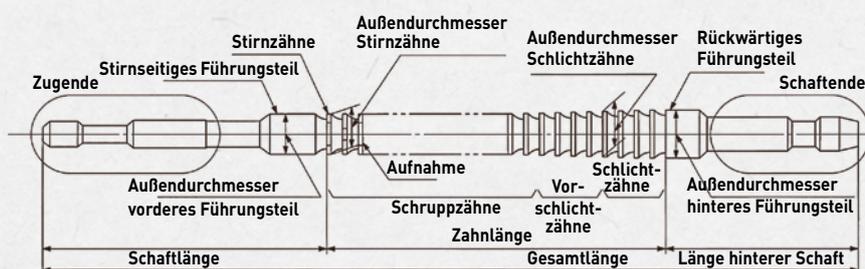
Bezeichnungen der Sektionen einer Räumnadel zur Innenbearbeitung
